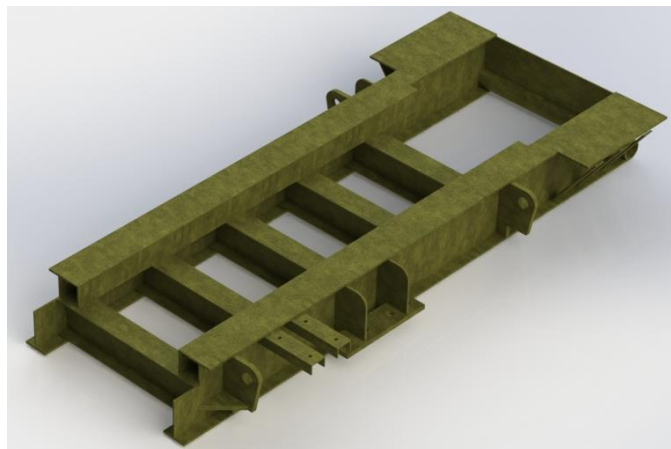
Estructura metálica tomada de las instalaciones de ATR S.A.S.
